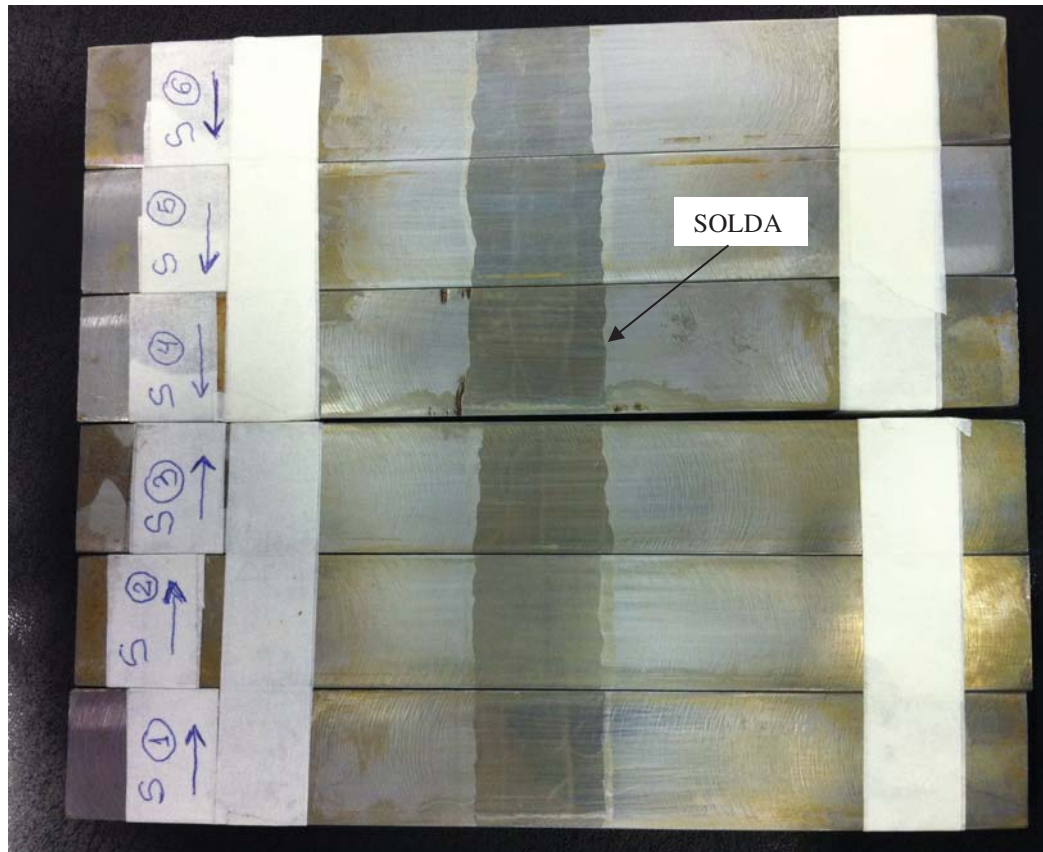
Corpos de prova SE (B) (solda) após o ataque químico. (Vista das faces)
